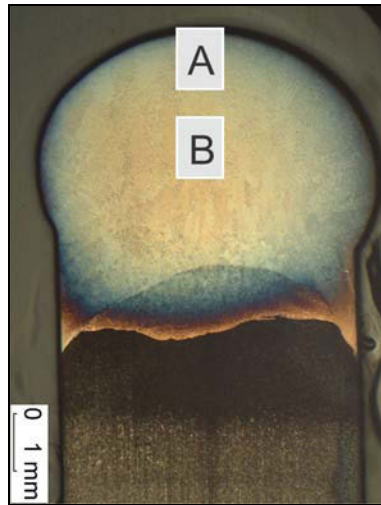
Übersichtsaufnahme der WIG-Wiederaufschmelzung der Legierung Cr8Ni12 (Probe aus In-situ-Beugungsexperiment), Lage der Mikroschliffbilder: A) Schweißgutoberfläche, B) Schweißgutmitte
